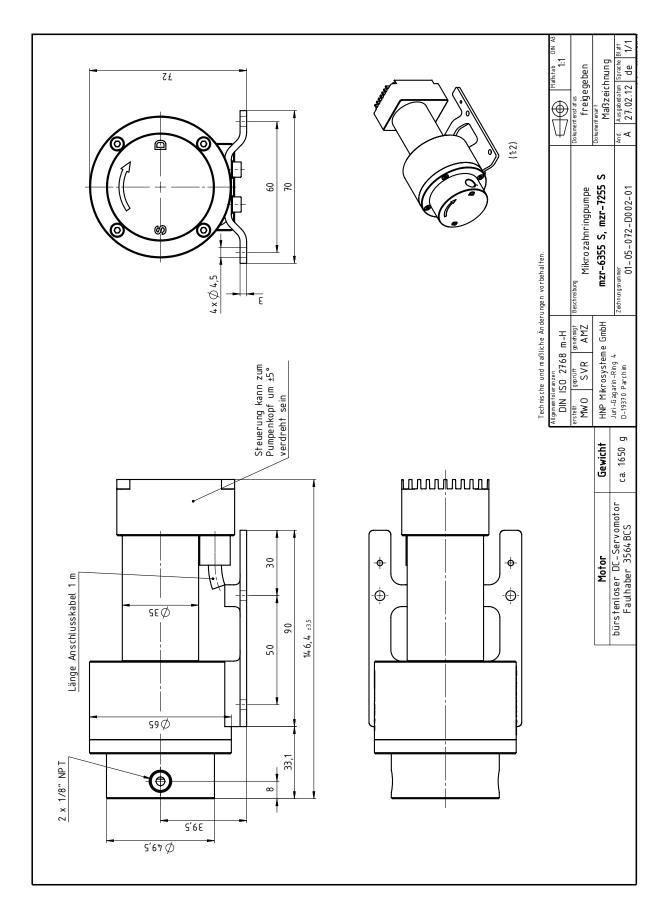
Masszeichnung Mikrozahnringpumpe mzr-6355/7255
